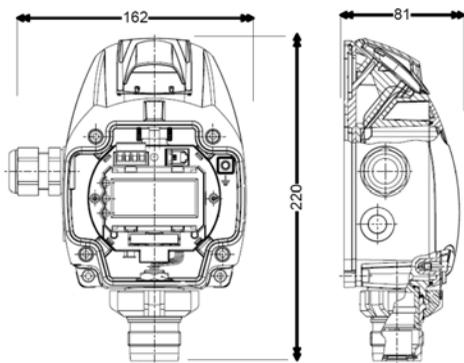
Dimensioni di ingombro Prima X I Pressacavo
